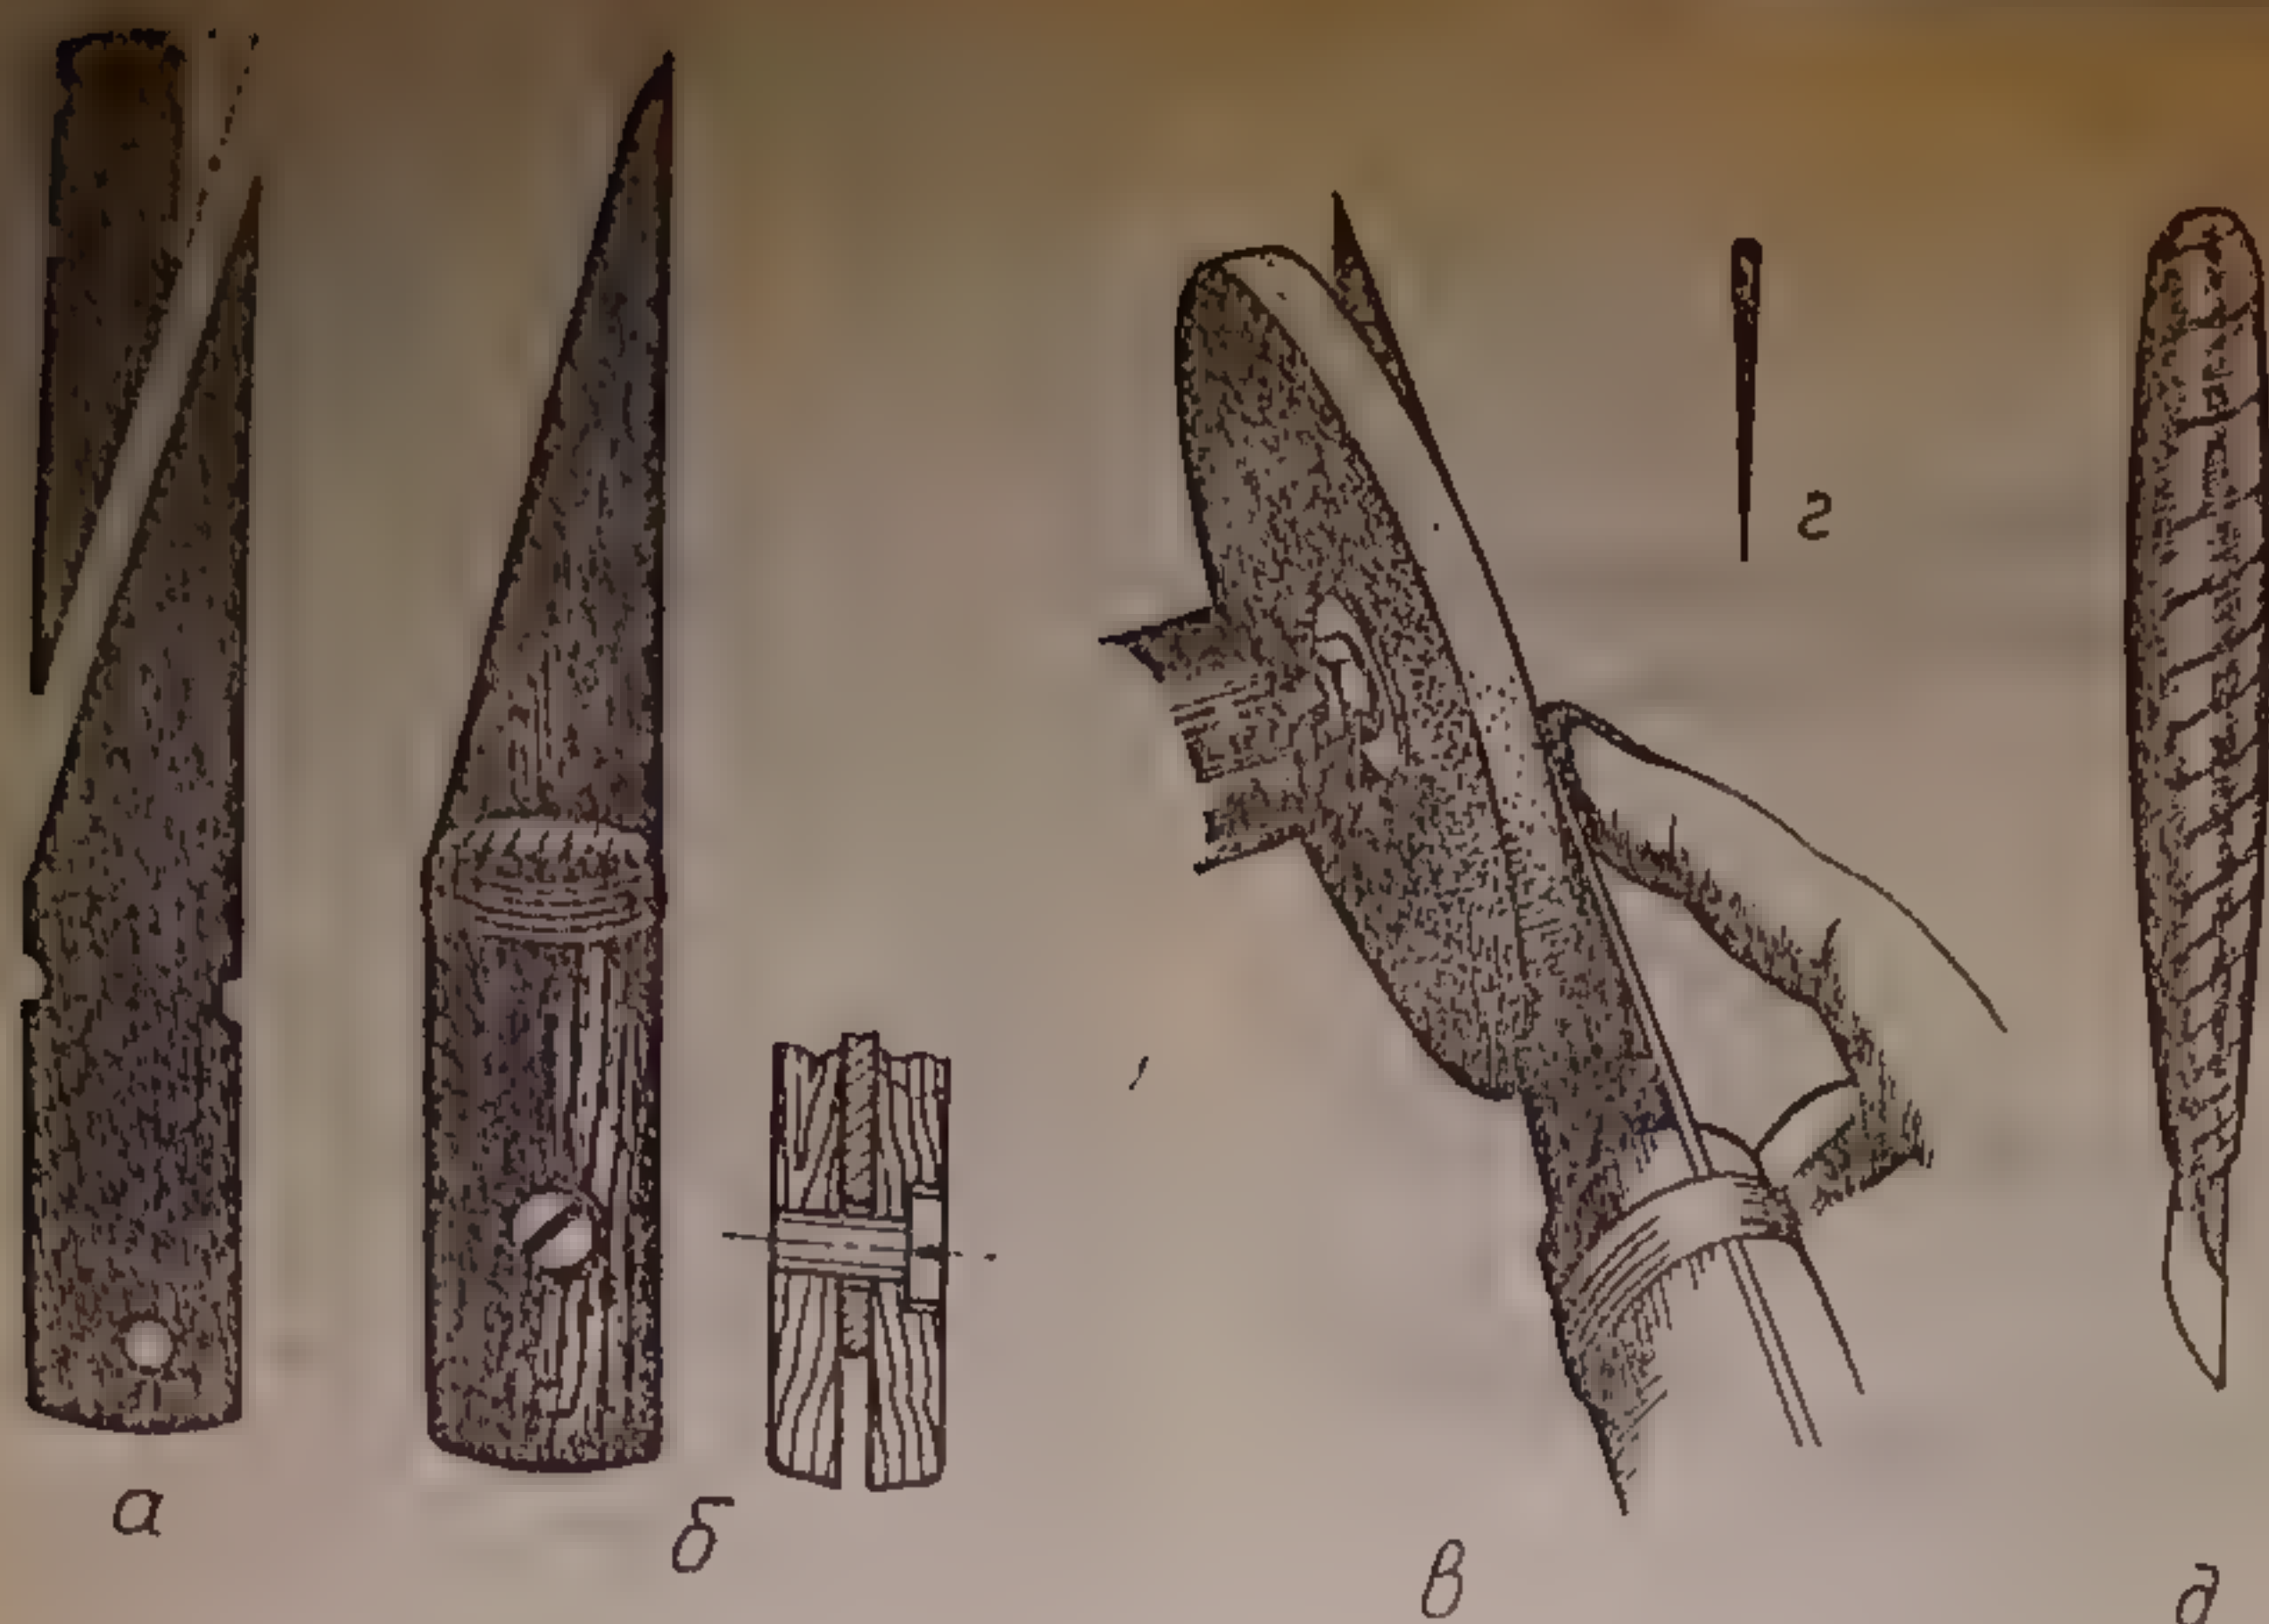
Ножи для резьбы: а — изготовление ножей из ножовочного полотна; б — устройство ручки; в — заточка ножа; г — поперечное сечение ножа; д — маленький ножик из надфиля
